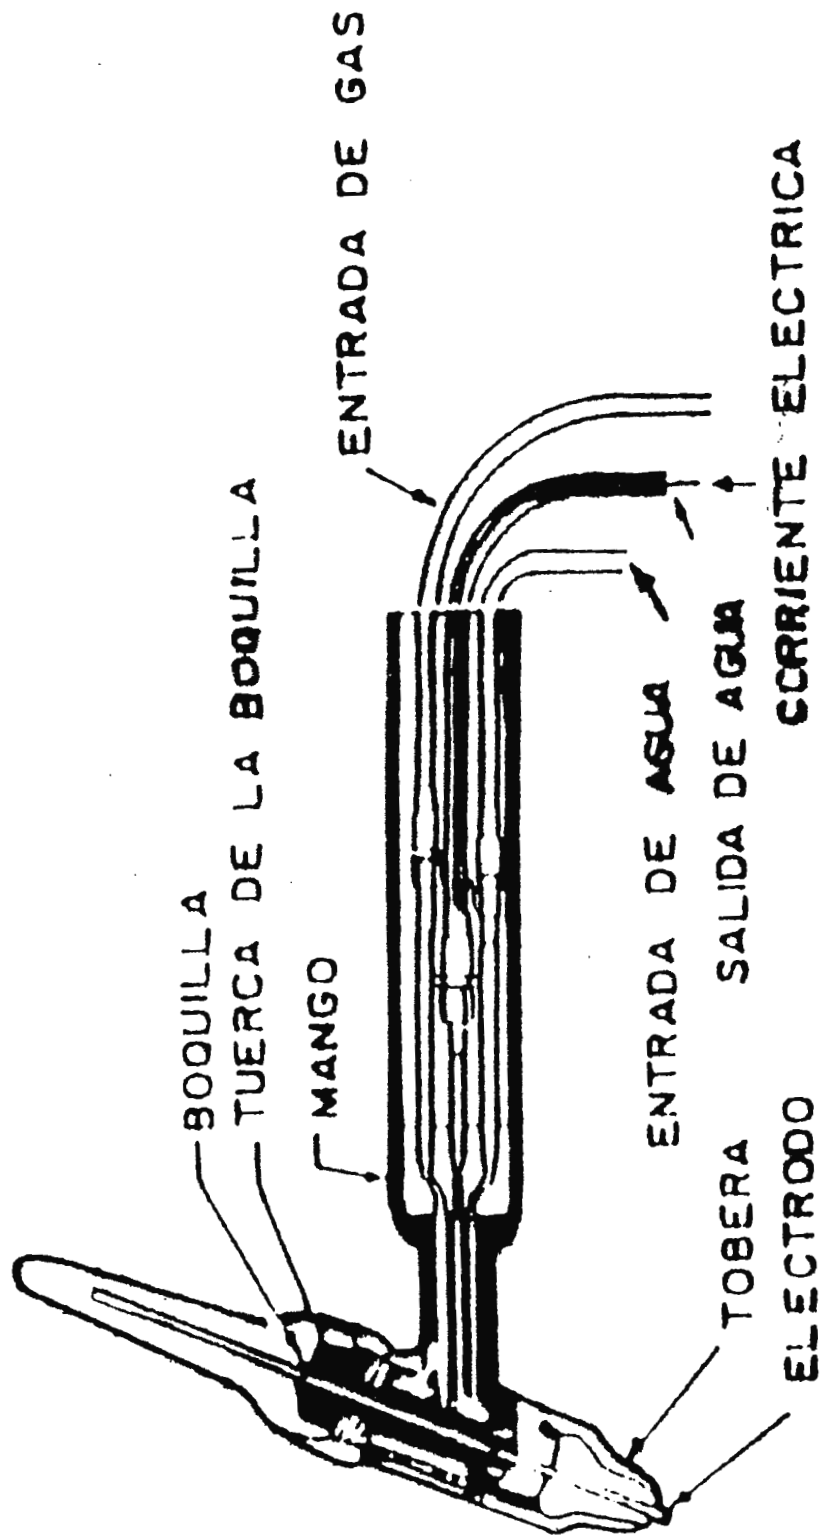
Partes de una pistola de soldar con proceso de soldadura T.I.G.
